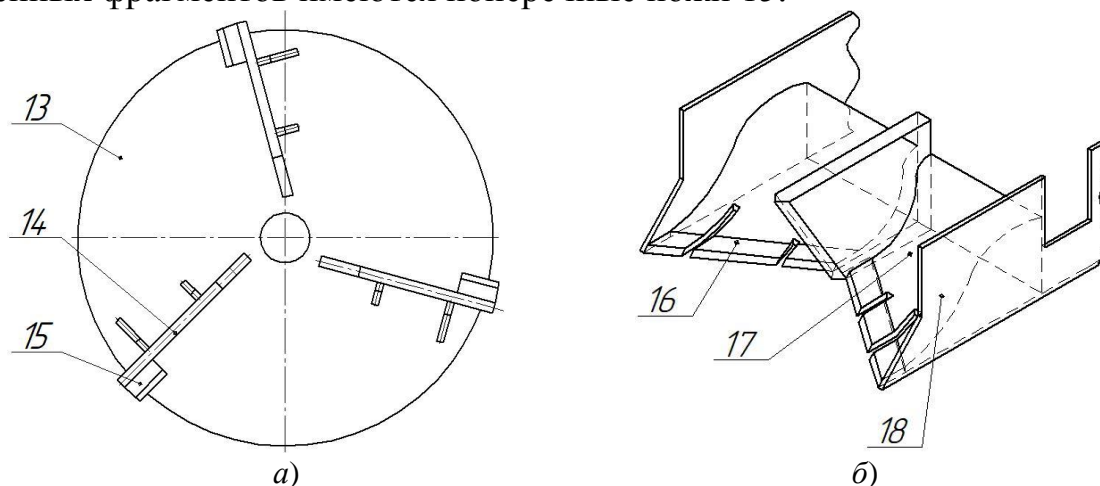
Конструктивные элементы полосопрокладывателя: а – фрезерный рабочий орган, б – поддон-рыхлитель
